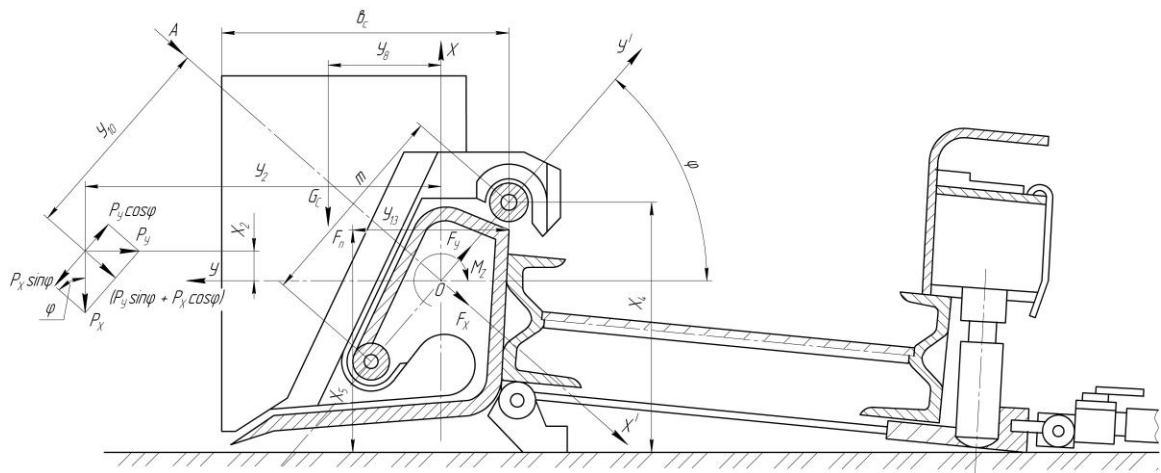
Вид сбоку исполнительного органа струговой установки скользящего типа
